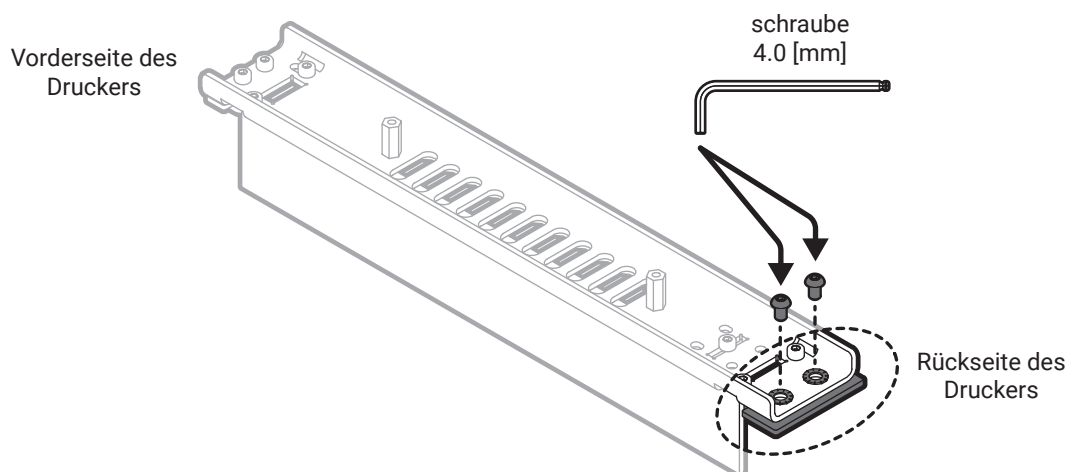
Schraube den Recoater Blade mit der Linearführungsscheibe fest an der Führung.
